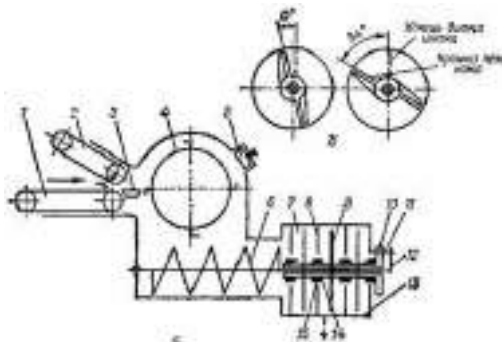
Конструктивно-функціональна схема (а) і схема регулювання ступеня подрібнення продукту (б) подрібнювача ИКВ-5А «Волгарь-5»: 1 - подавальний транспортер; 2 - пресувальний транспортер; 3 - протирізальна пластина; 4 - ножовий барабан; 5 - заточувальний пристрій; 6 - шнек; 7 – апарат вторинного різання; 8 - нерухомий ніж; 9 - рухомий ніж; 10 - туллка; 11 - зрізний штифт; 12 - фланець вала шнека; 13 - опора нерухомих ножів; 14 - прокладка; 15 - кільце.
